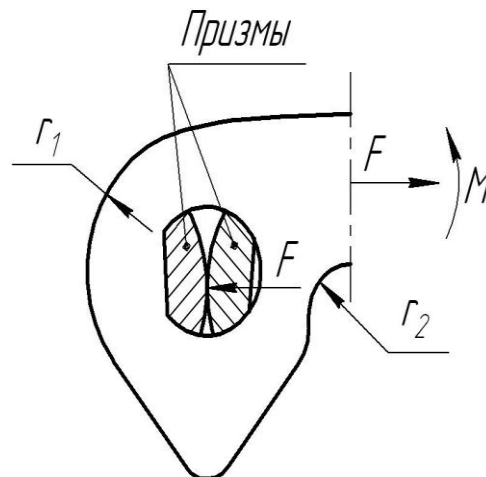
Пластина стандартизованной зубчатой цепи
